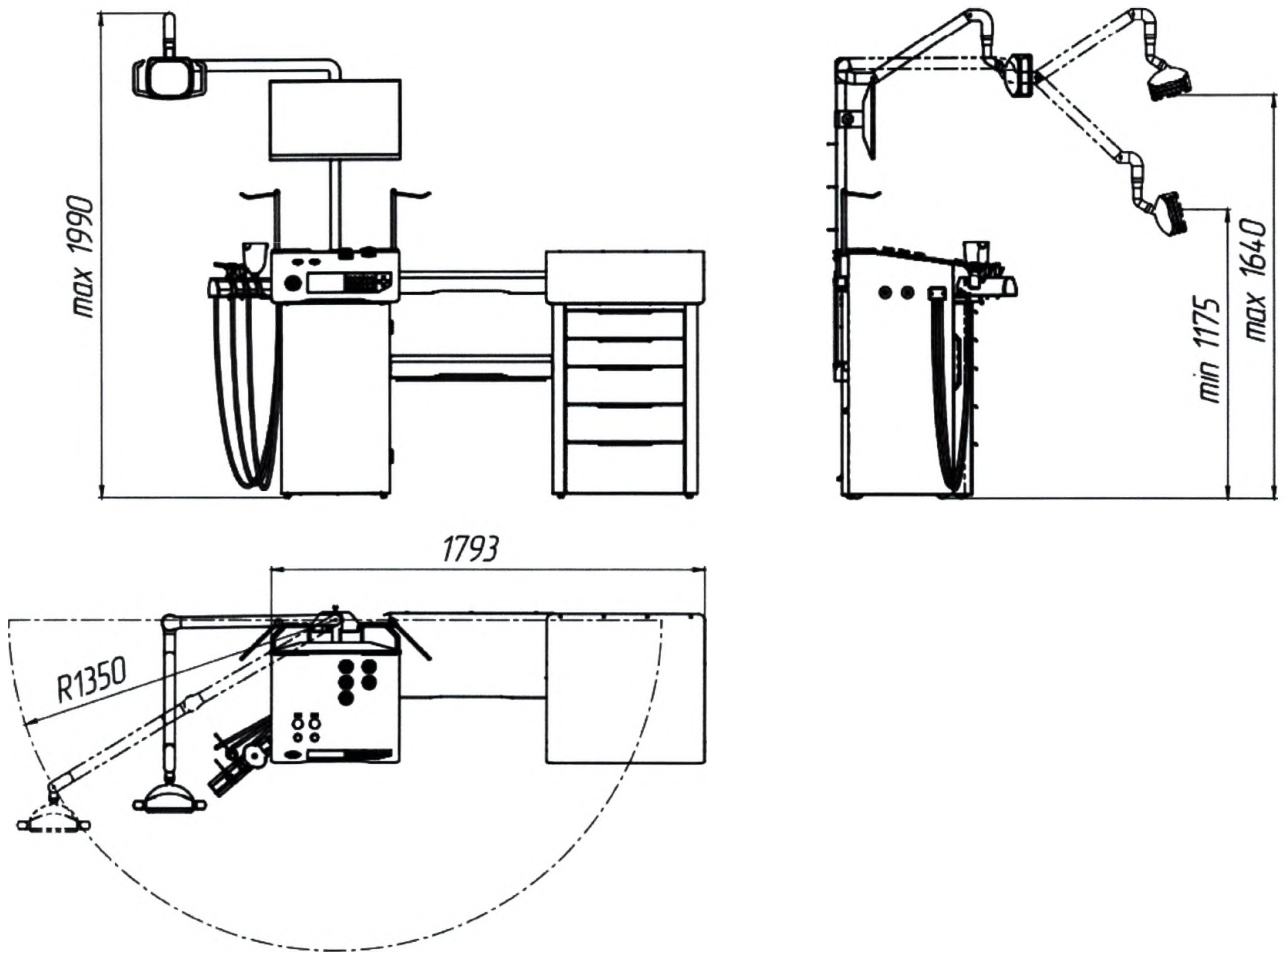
Габаритный чертеж ЛОР-комбайна в сборе
